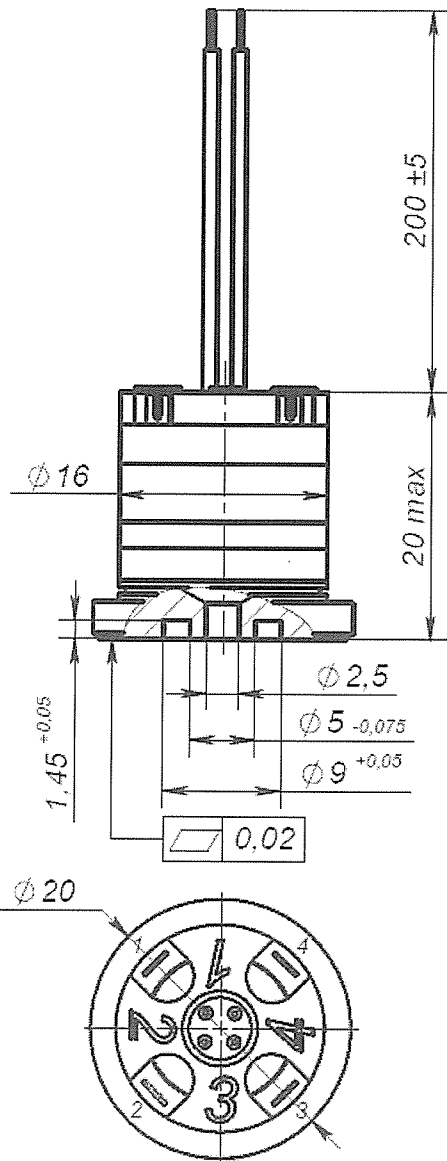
Габаритные и присоединительные размеры тензопреобразователя ДД2,5П-1;
